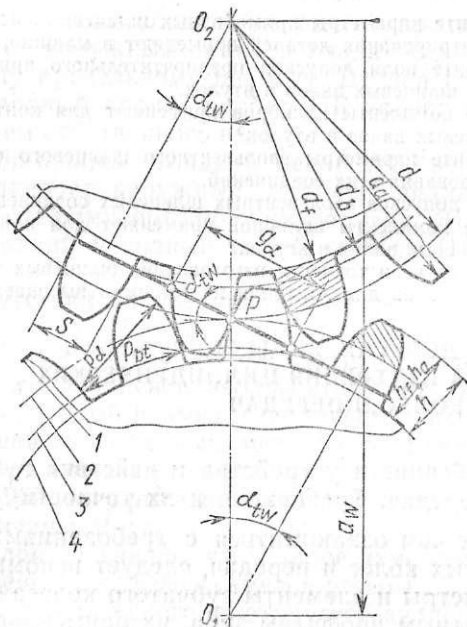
Параметры эвольвентного зубчатого колеса и передачи:
